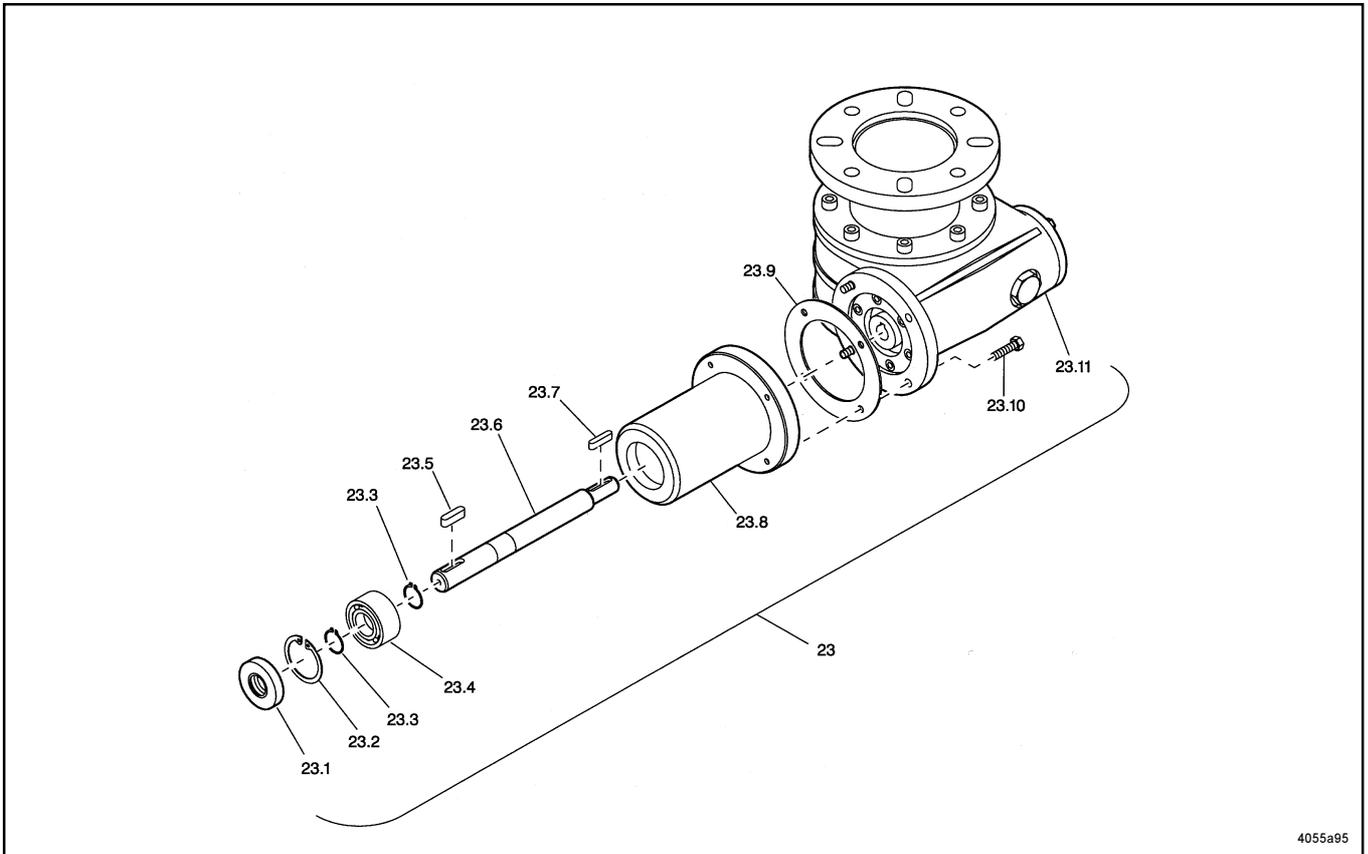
Pièces pour commande "bout d'arbre nu"
